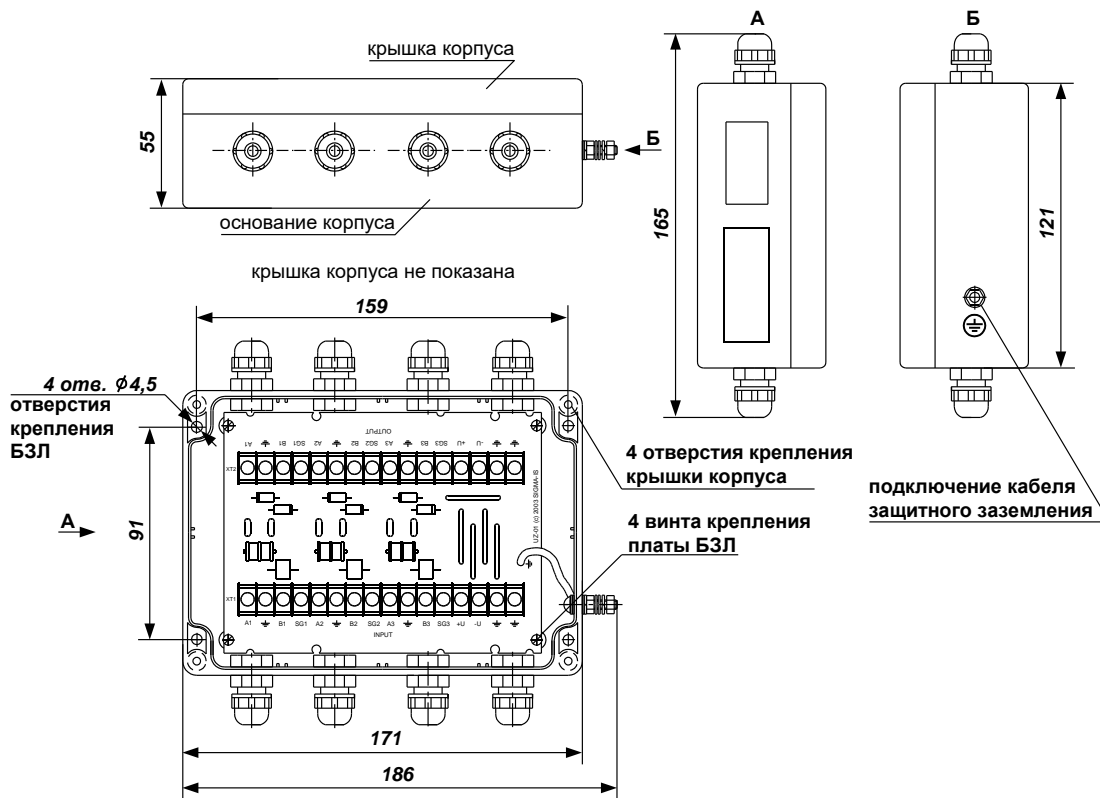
Габаритные и присоединительные размеры БЗЛ-01, БЗЛ-04
